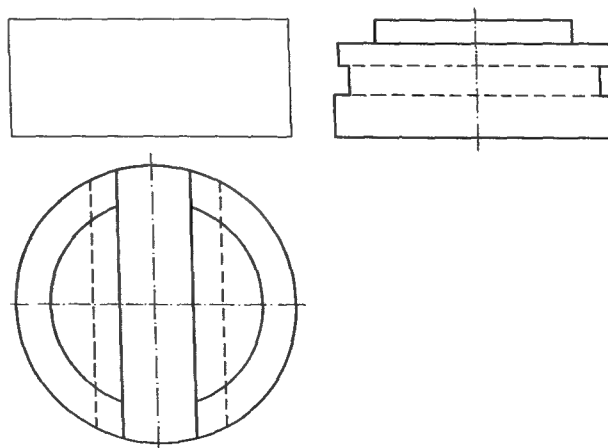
Dibujar el alzado del objeto del que se dan planta y perfil.
